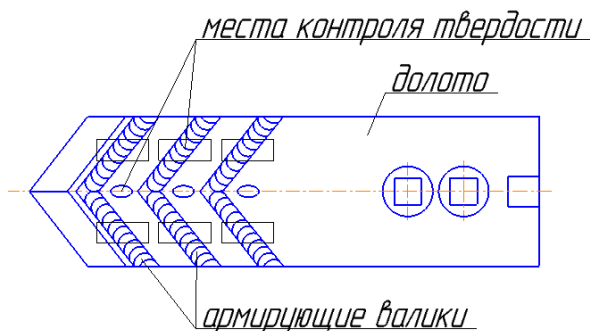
Схема наплавки на рабочей поверхности параллельно периметру заглубляющей части и места контроля твердости
